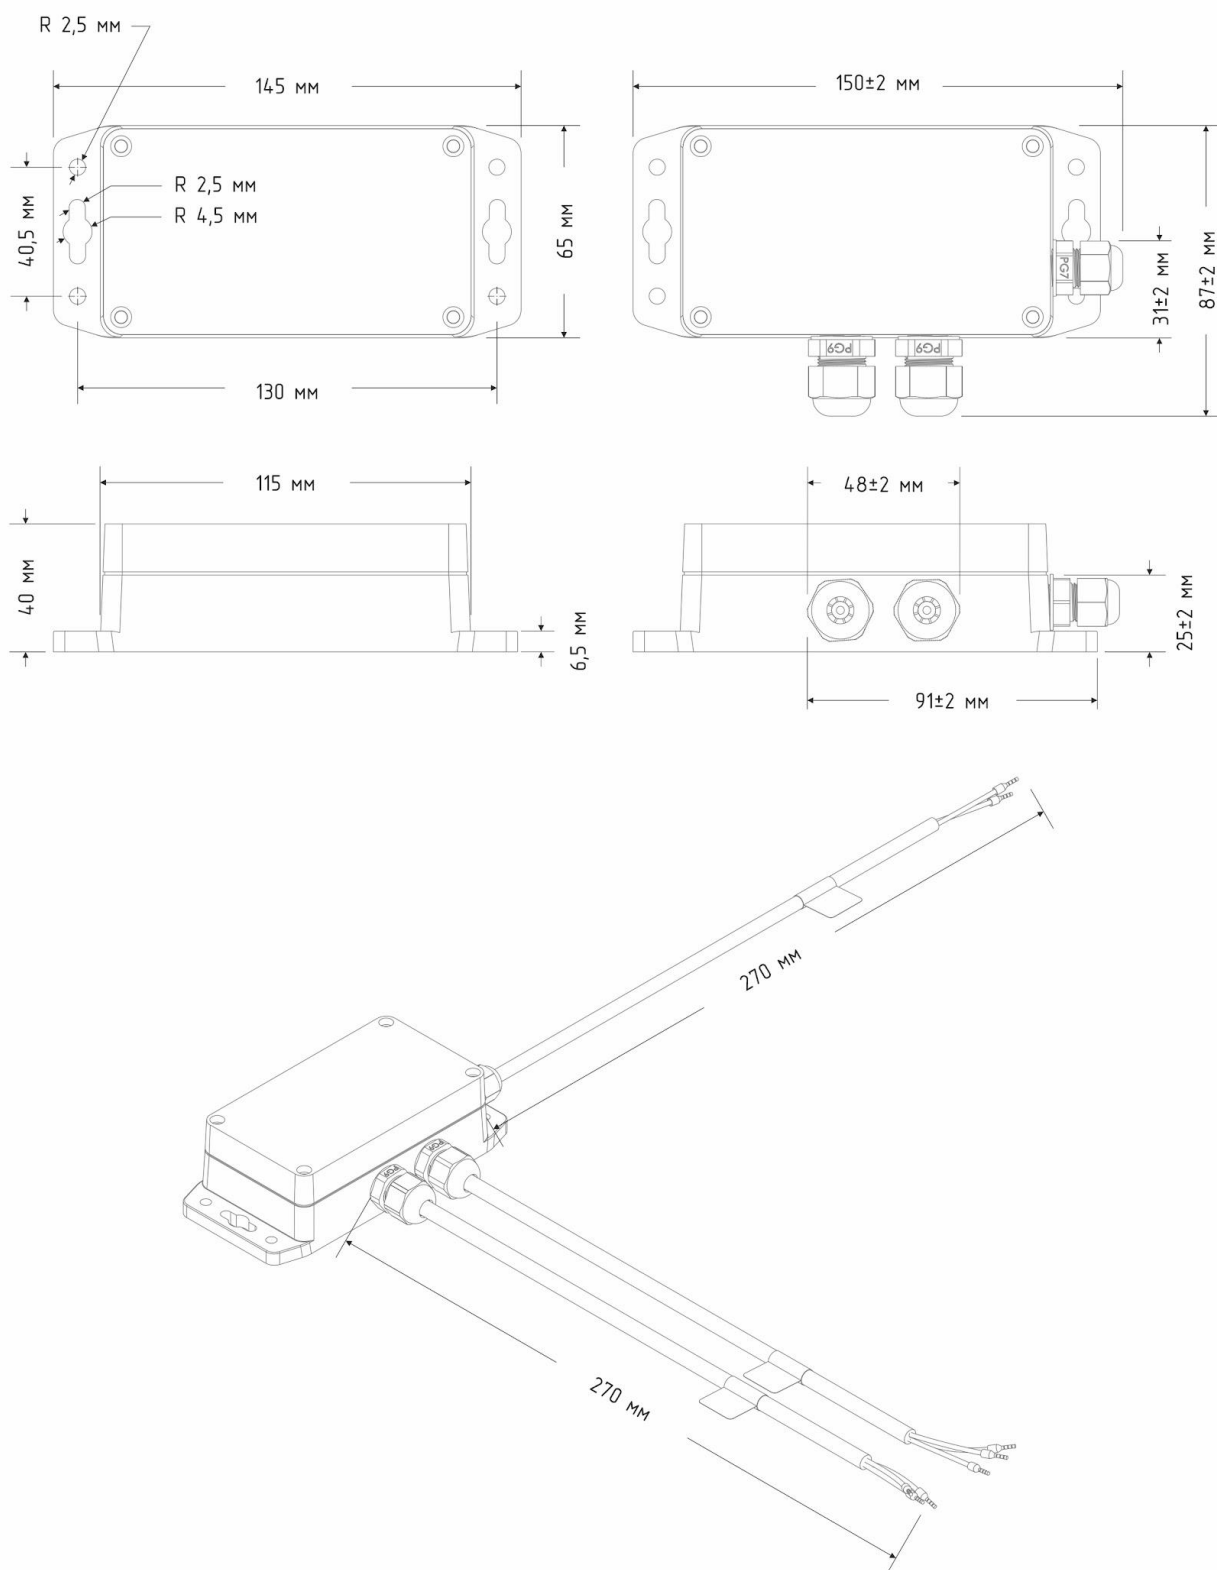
Контроллер SR в корпусе IP65 (с фланцем).
